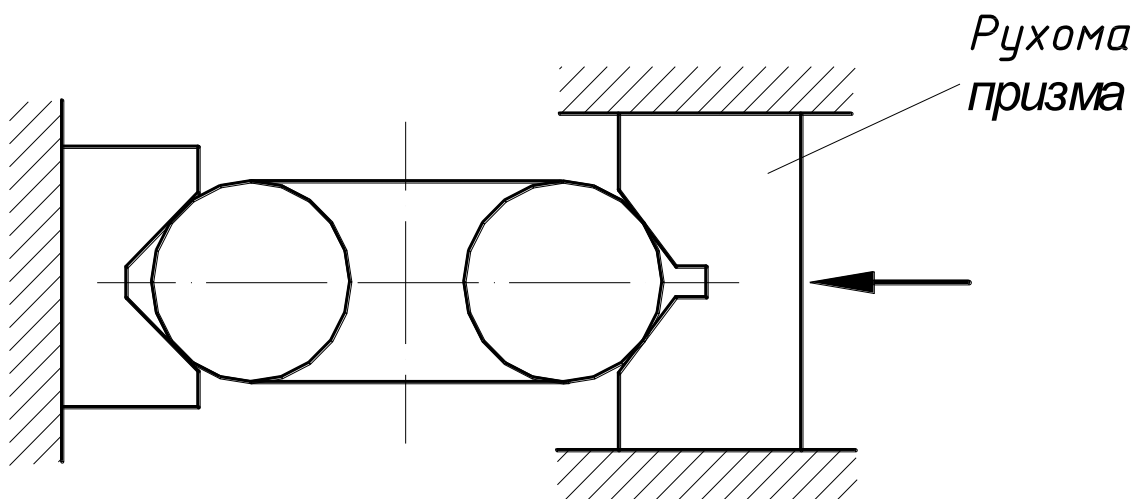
Схема встановлення заготовки із застосуванням рухомої призми
